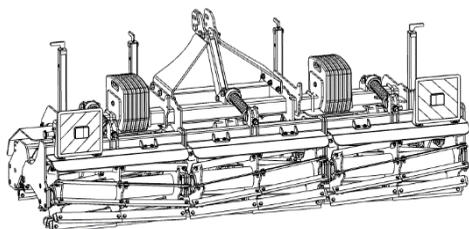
Beispiel für die korrekte Befestigung von Gewichten.
